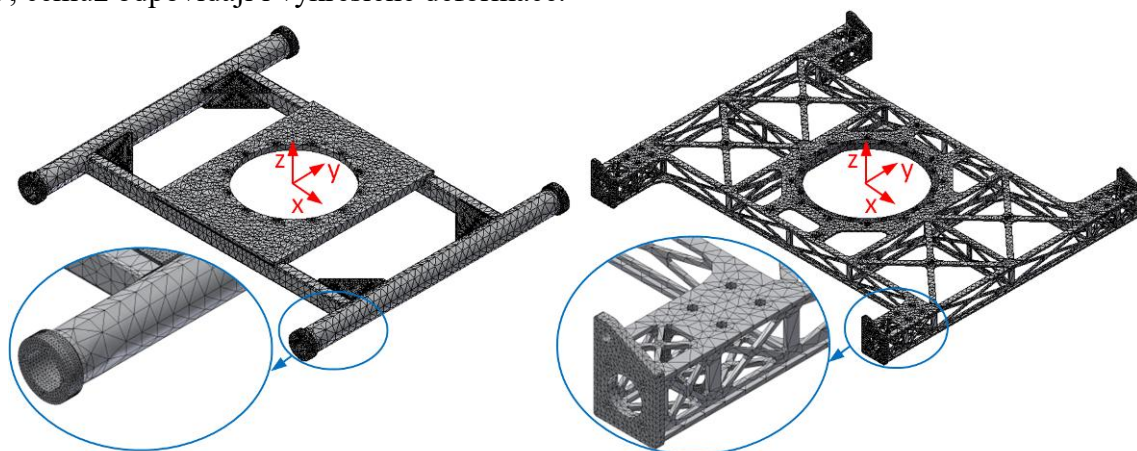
Vyobrazení 3D modelu původní a nové soustavy rámu robotu
